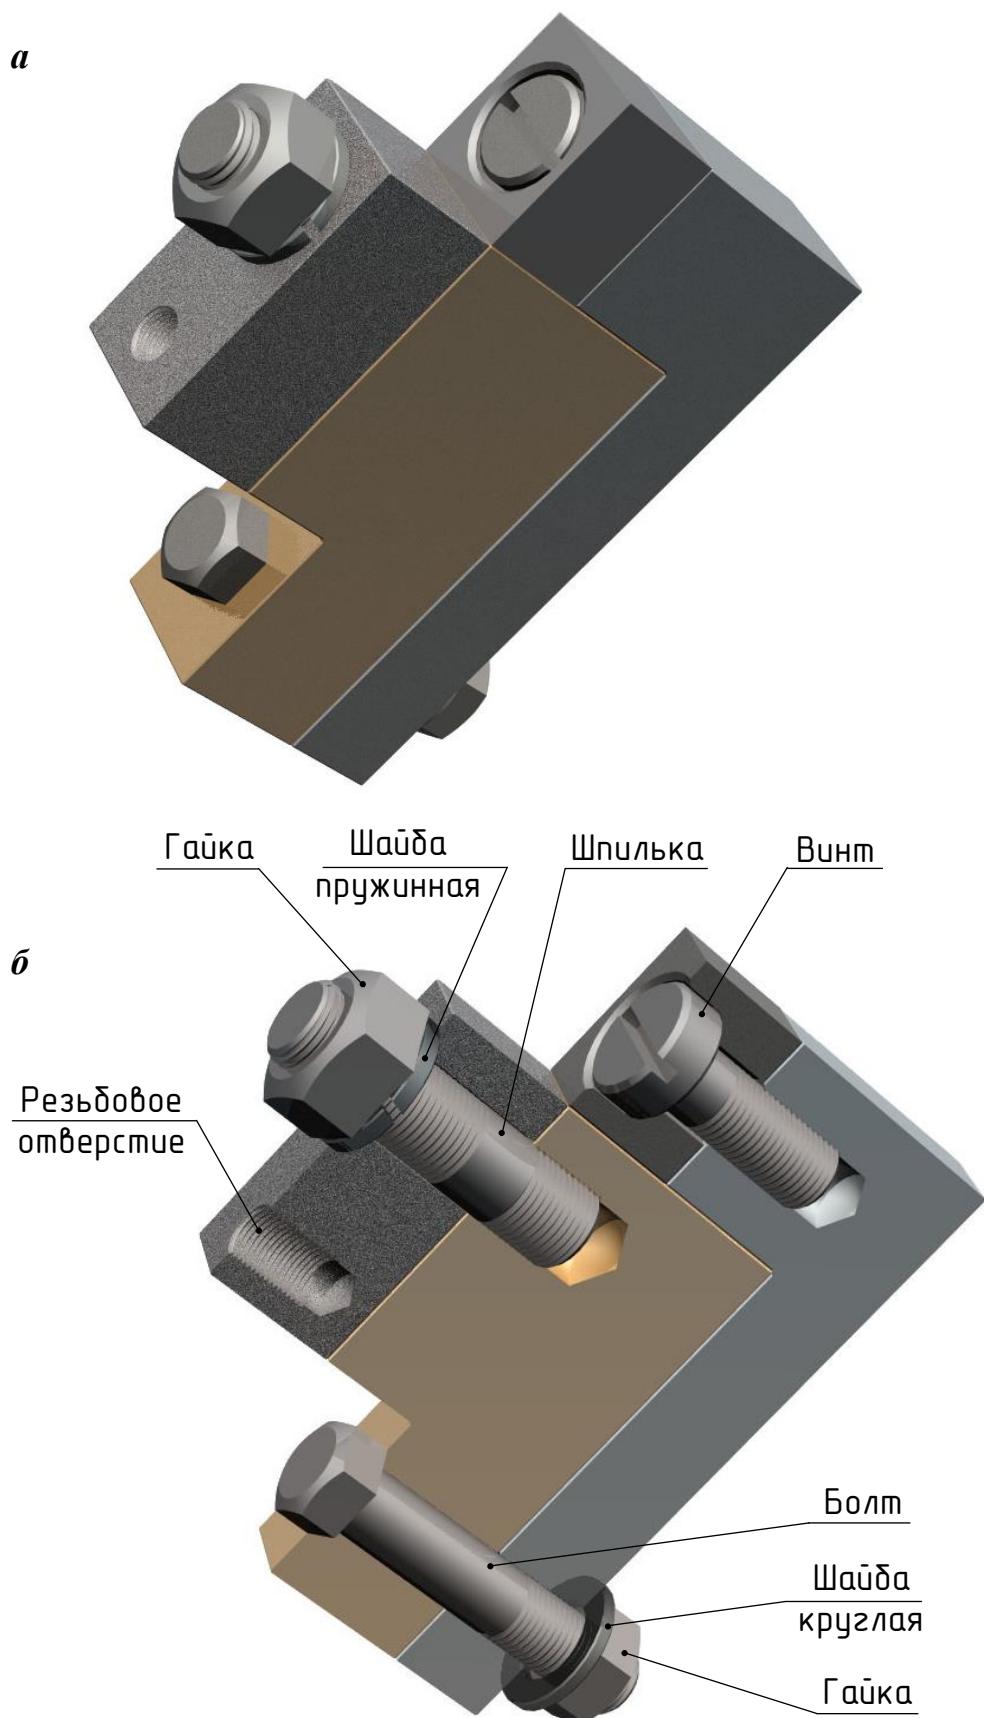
Резьбовое соединение деталей стандартными крепежными изделиями (винтом с цилиндрической головкой; шпилькой с пружинной шайбой; болтом с круглой шайбой): а – внешний вид соединения; б – условный разрез соединения по осям резьбовых изделий
